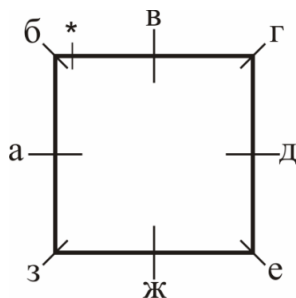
Схема последовательности измерений толщины корочки заготовки
